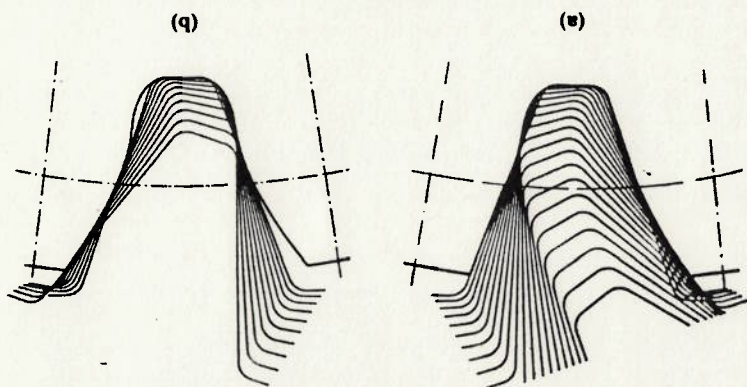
Geração dos dentes de uma engrenagem através de usinagem com "fresa-caracol".
